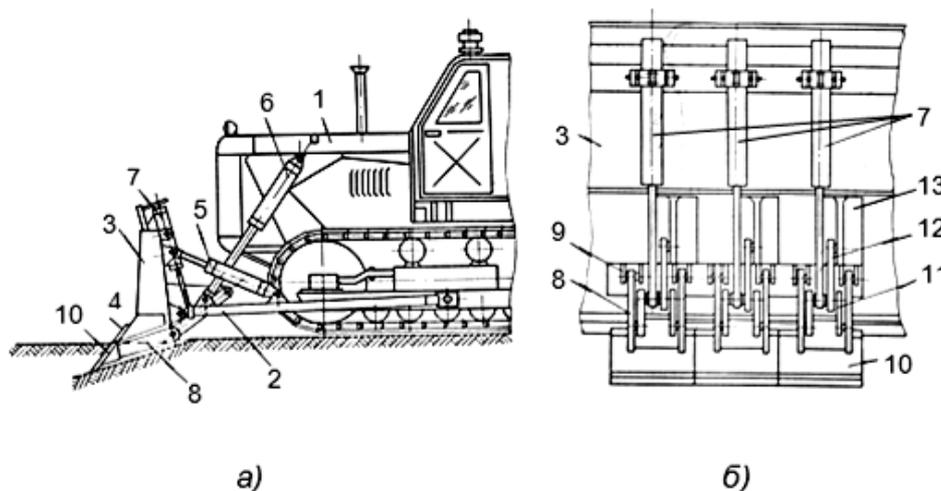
Бульдозер с дополнительным режущим ножом: вид сбоку (а), вид сзади (б): 1 - базовый трактор; 2 - толкающие брусья; 3 - отвал; 4 - режущий нож; 5 и 6 – гидроцилиндры управления; 7 - гидроцилиндры для поворота кронштейнов; 8 - кронштейны; 9 - шарниры; 10 - дополнительный нож; 11 и 12 - рычаги; 13 - кронштейн
